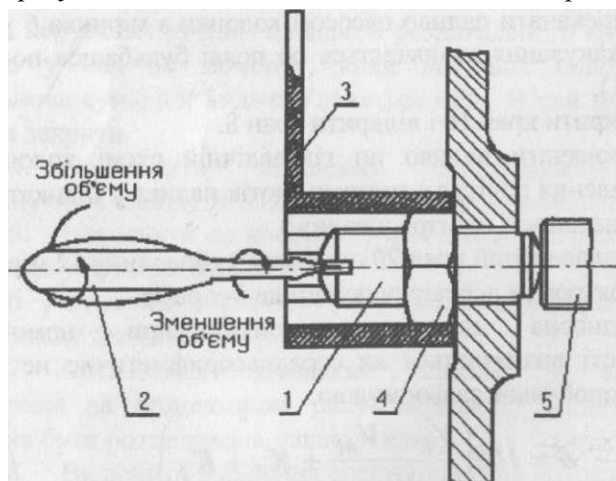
Схема регулювання лічильника рідини: 1- регулювальний гвинт; 2- викрутка; 3- ключ; 4- контргайка; 5- упор поршня.
